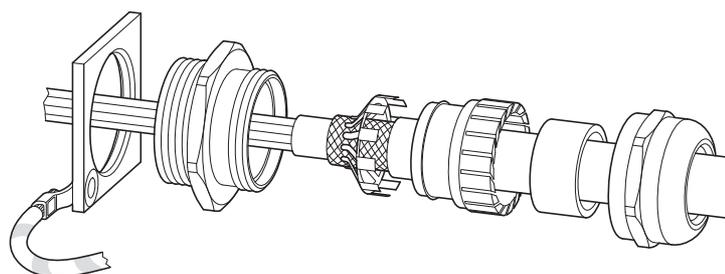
Beispiel: Aufbau der EMV-Verschraubung
